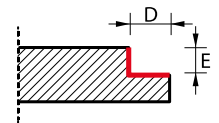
Фреза для обработки кромки Модель 12-690-000-00003 диаметр 80/9
